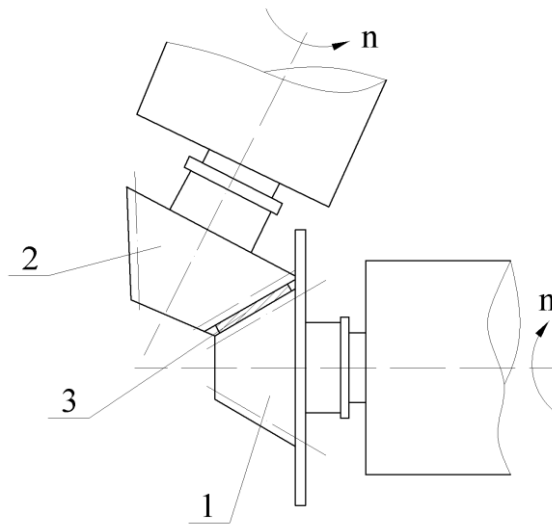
Схема формоутворення гофрованої поверхні кінчними колесами:
